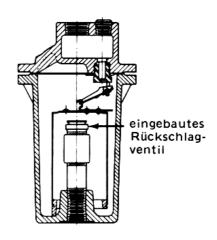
Eingebautes Rückschlagventil mit Leitrohr und Muffe.
